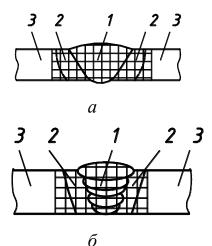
Макрошлифы сварных соединений с координатной сеткой (1 - uos; 2 - 3TB; 3 - ocнoвной металл):
